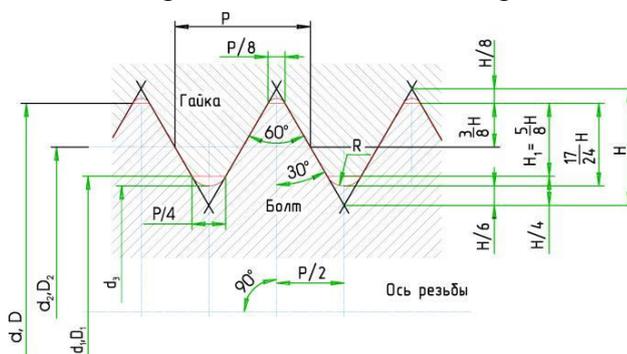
ГОСТ 24705.81 Основные размеры
